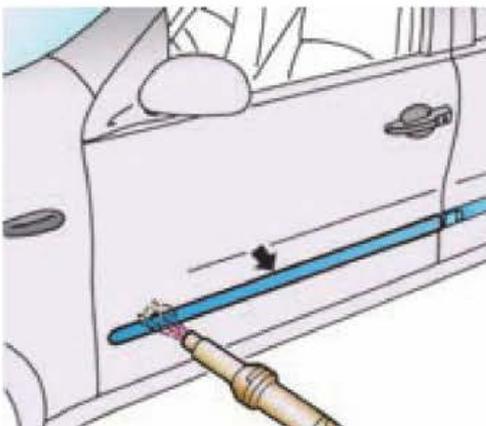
Calentamiento de la moldura para reblandecer el adhesivo.
